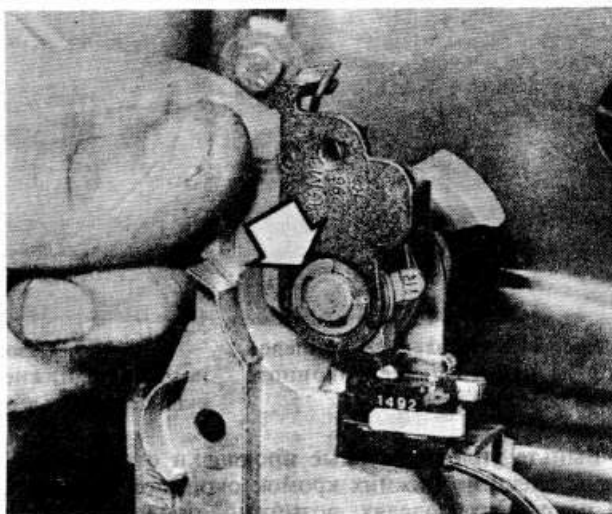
Стопорное кольцо цилиндра замка передней двери
